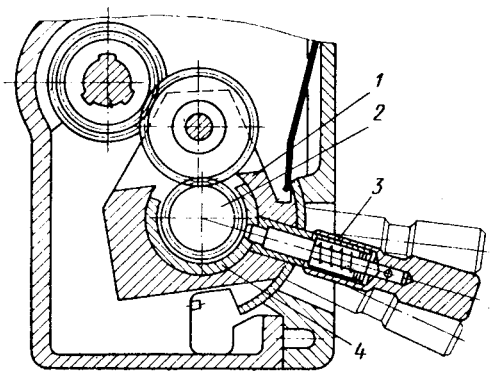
Коробка подачи станка SV18R (Чехословакия)
